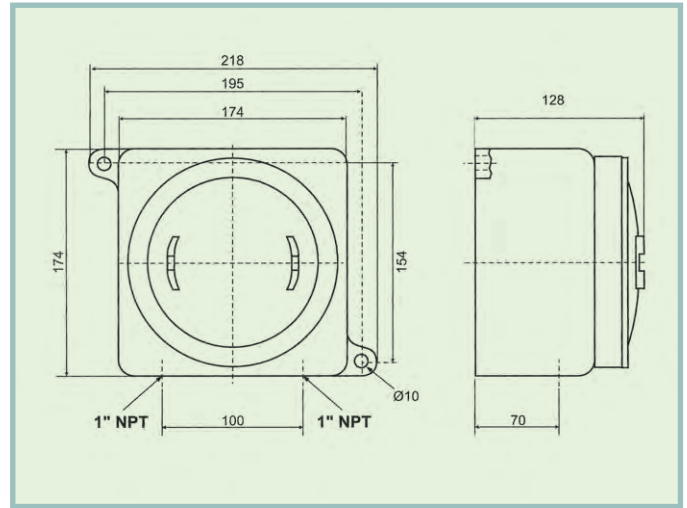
Габаритный чертёж источника питания RSxx-PSD-Ex4.34CON
